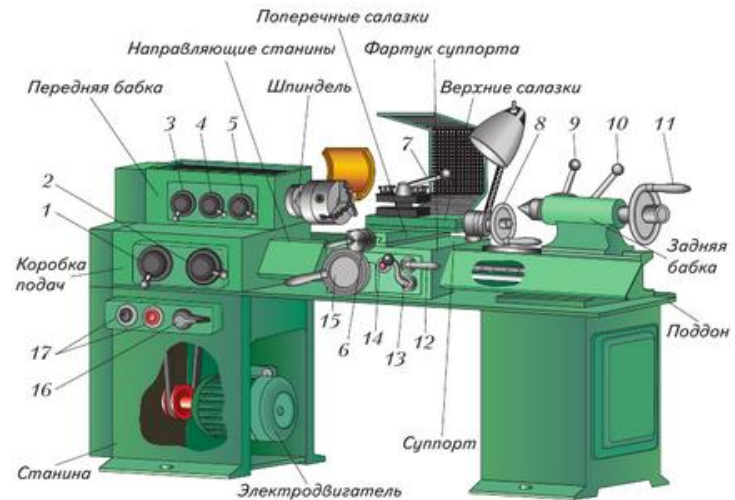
Токарно-винторезный станок ТВ-6: 1, 2 — рукоятки переключения величины подачи; 3 — рукоятка переключения гитарного механизма; 4, 5 — рукоятки переключения частоты вращения шпинделя; 6 — рукоятка поперечной подачи суппорта; 7 — рукоятка закрепления резцедержателя; 8 — рукоятка перемещения верхних салазок; 9 — рукоятка крепления пиноли; 10 — рукоятка крепления задней бабки; 11 — маховик подачи пиноли; 12, 13 — рукоятки управления механической подачей; 14 — кнопка включения ременной передачи; 15 — маховик перемещения суппорта; 16 — рукоятка реверса; 17 — кнопки включения и отключения электродвигателя
